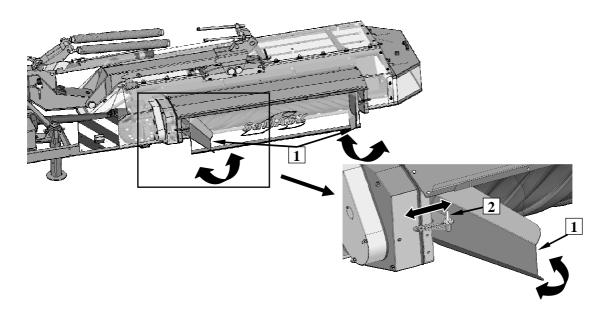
Regulierung der Schwadformer: 1-Schwadformer, 2-Regelschraube
